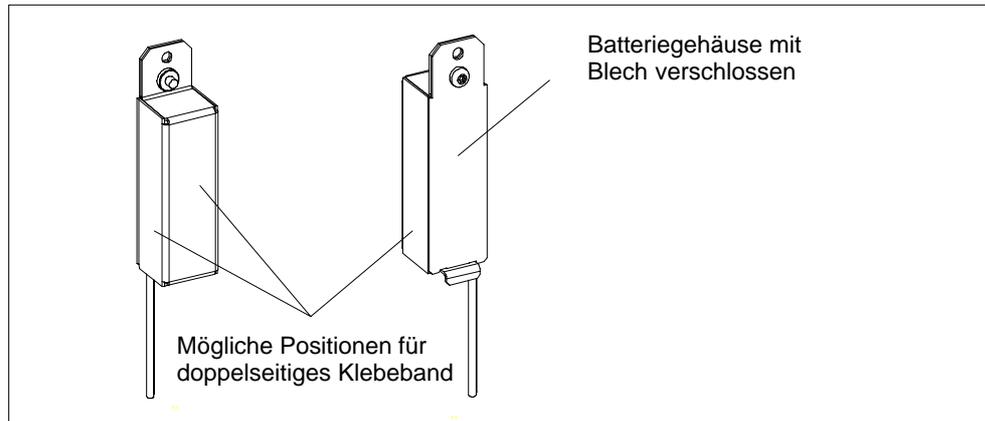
Blech für Batteriehalterung am PC-Gehäuse
